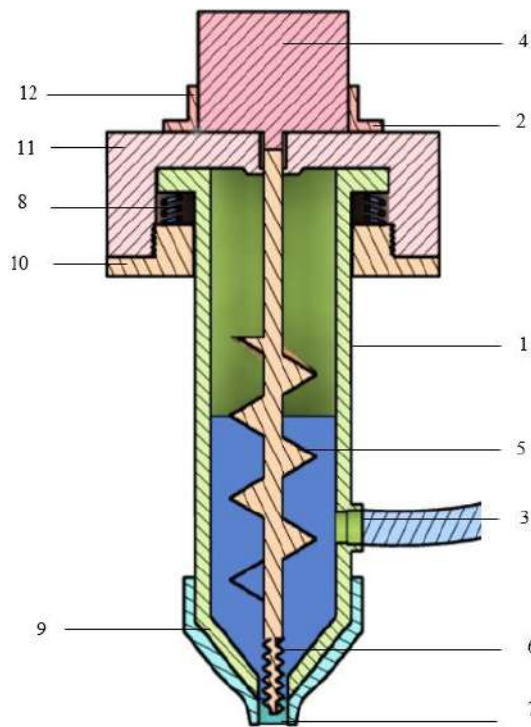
Экструдер для подачи смеси (пасты), содержащей до 30 % опилок и связующее: 1 – корпус; 2 – крепление; 3 – отверстие для загрузки (подачи) в экструдер; 4 – привод; 5 – шнековая мешалка; 6 – дозатор; 7 – сопло; 8 – пружина; 9 – нагревательный элемент; 10 – прижим; 11 – поддержка экструдера; 12 – крепления [107]
